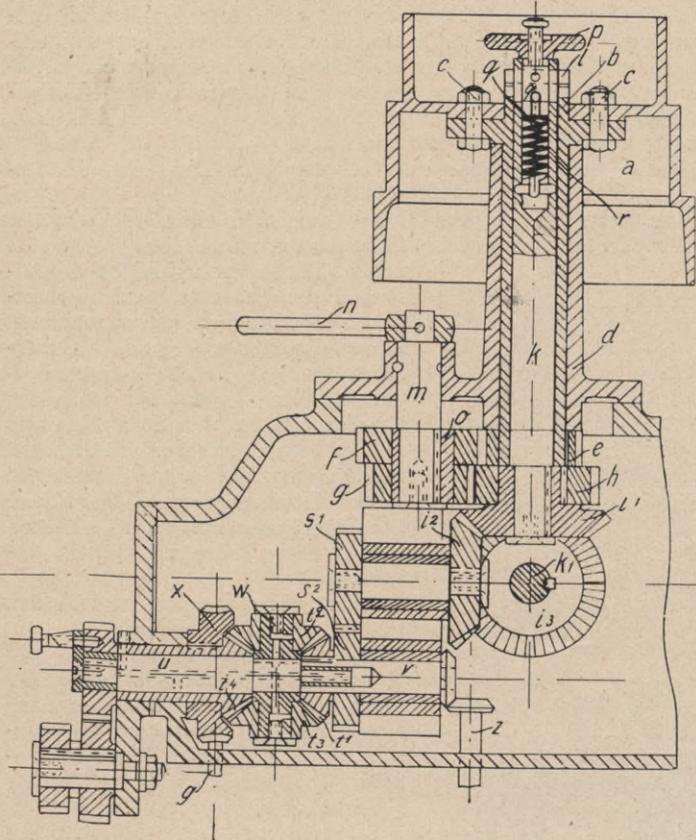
Das im Innern der Abwälz-Fräsmaschine gelagerte Getriebe mit Stufenscheibe und Differentialgetriebe
